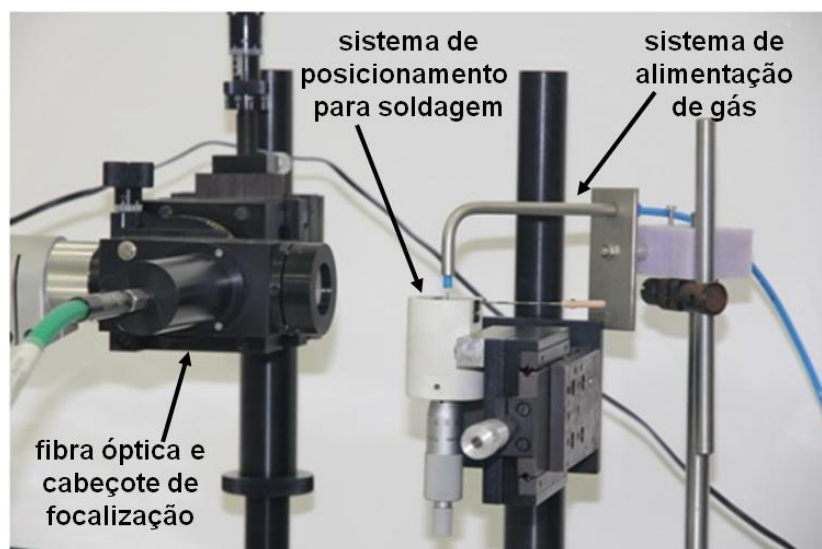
Dispositivo de soldagem estático em detalhe
